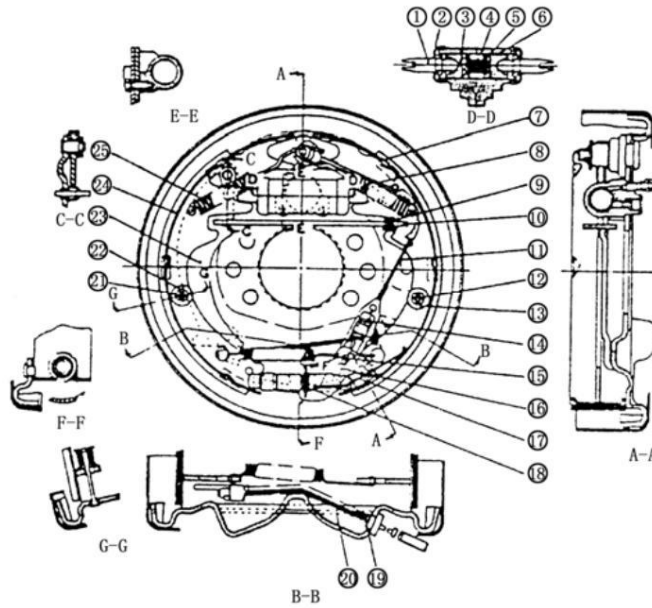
Freno de rueda de 1-1,8 t (izquierda)
